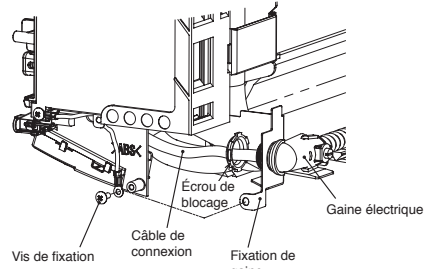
Construction du RAS-15, 17, 22LKV-UL
